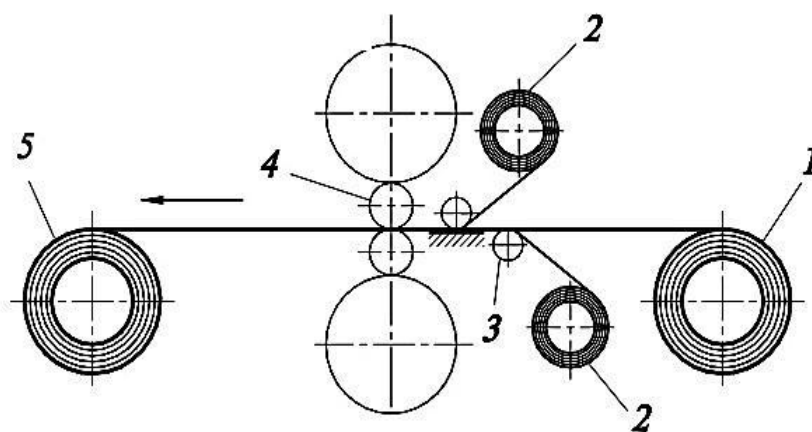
Рулонная прокатка трехслойного биметалла
